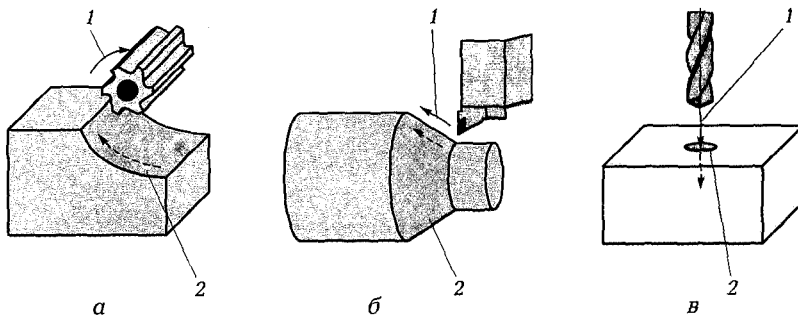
Движение инструмента при фрезеровании (а), точении (б) и сверлении (в):
